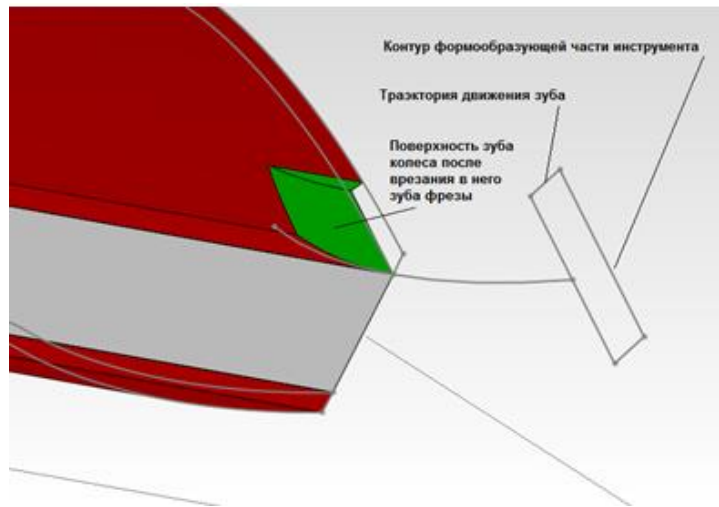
Формирование шероховатости поверхности зубьев колеса после врезания в него зуба фрезы
